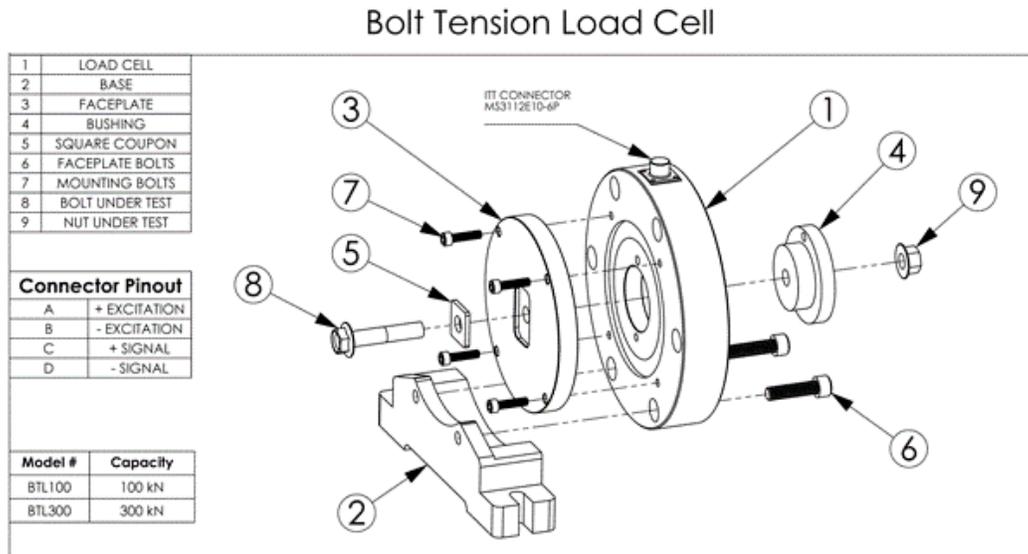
Ensamble de la celda de carga del equipo MC900
